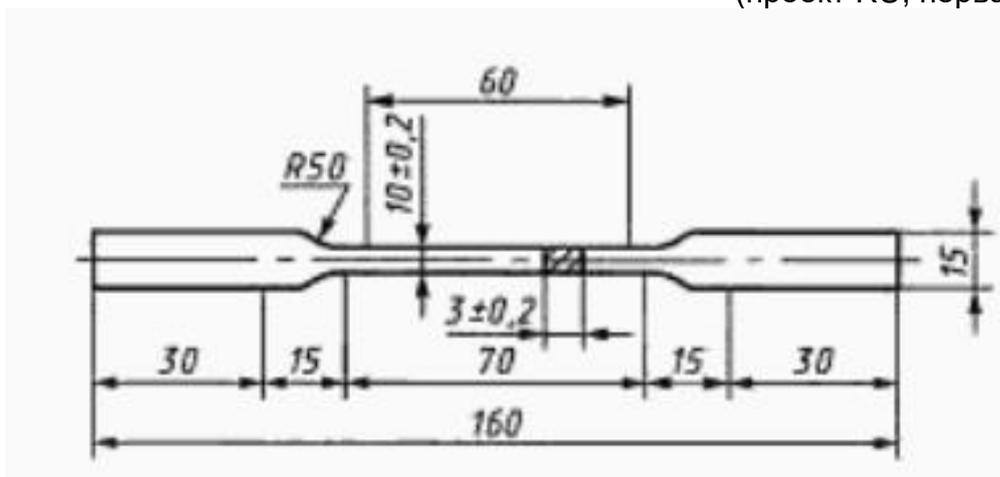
Формы и размеры (в миллиметрах) образца при литье под давлением
